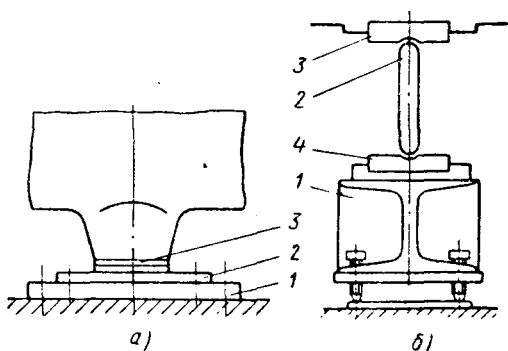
Скользящая (а) и качающаяся (б) опоры цилиндров:
